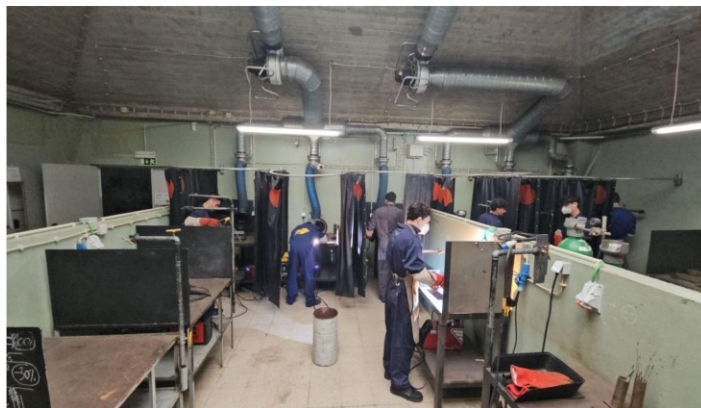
Aula de Soldadura Eléctrodo Revestido (SER)
